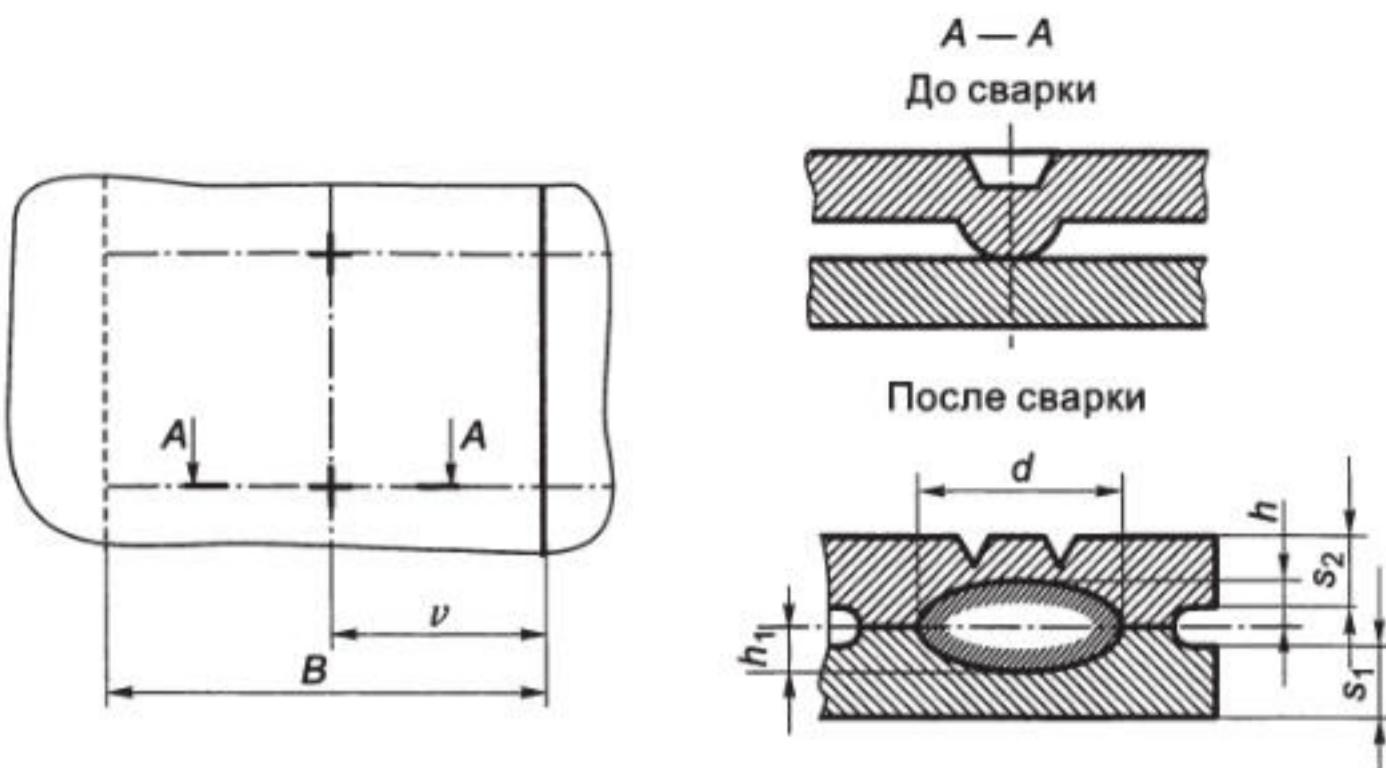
Конструктивные элементы соединений контактной рельефной сваркой
